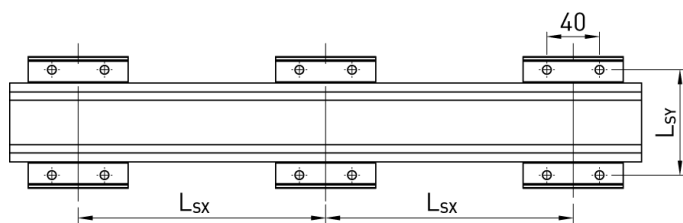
Rozstaw otworów przy bocznym mocowaniu modułów liniowych HM-B za pomocą profili mocujących
